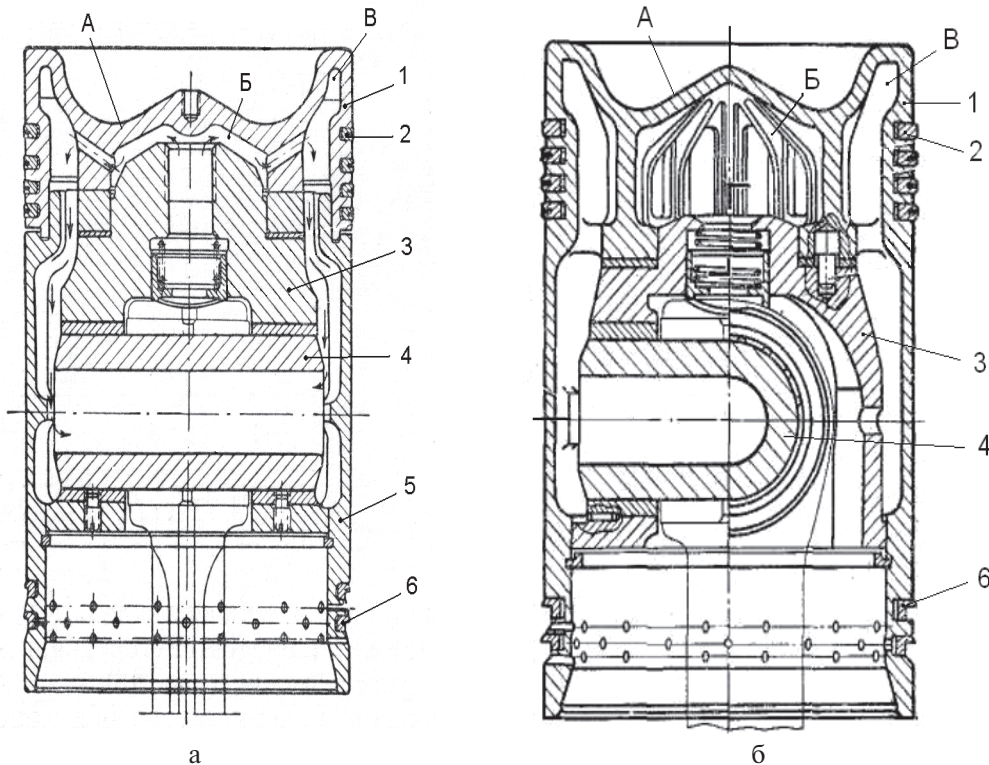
Поршень дизеля 11Д45: а) исходная конструкция (1959 г.); б) цельнолитой конструкции ВНИИЖТ. 1 – головка; 2 – кольцо компрессионное; 3 – вставка; 4 – поршневой палец; 5 – тронк; 6 – кольцо маслосъёмное; А – днище, Б – внутренняя полость, В – боковой карман.
